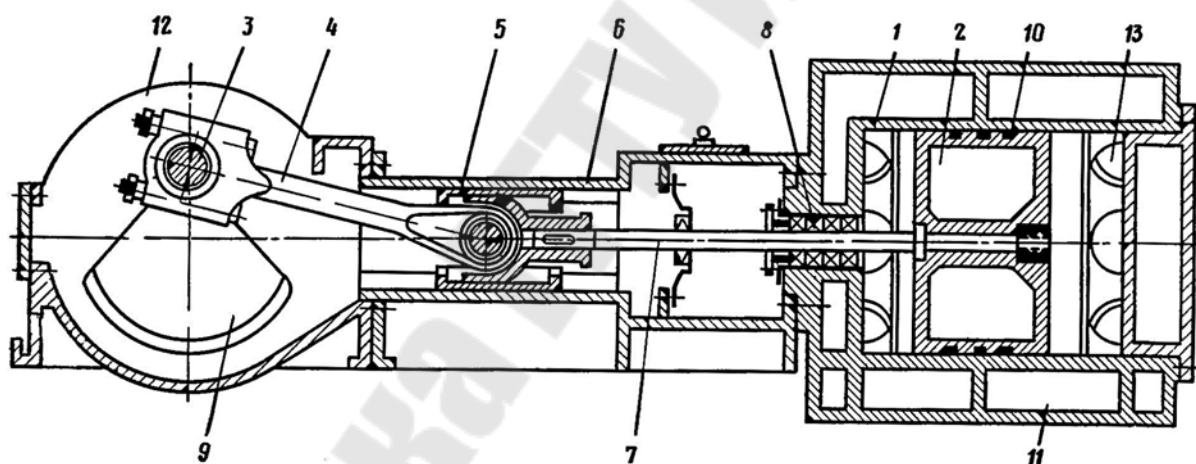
Продольный разрез одноступенчатого поршневого компрессора: 1 – цилиндр; 2 – поршень; 3 – коленчатый вал; 4 – шатун; 5 – ползун; 6 – направляющие; 7 – шток; 8 – сальник; 9 – противовес; 10 – поршневые кольца; 11 – водяная рубашка; 12 – кожух; 13 – клапан.
